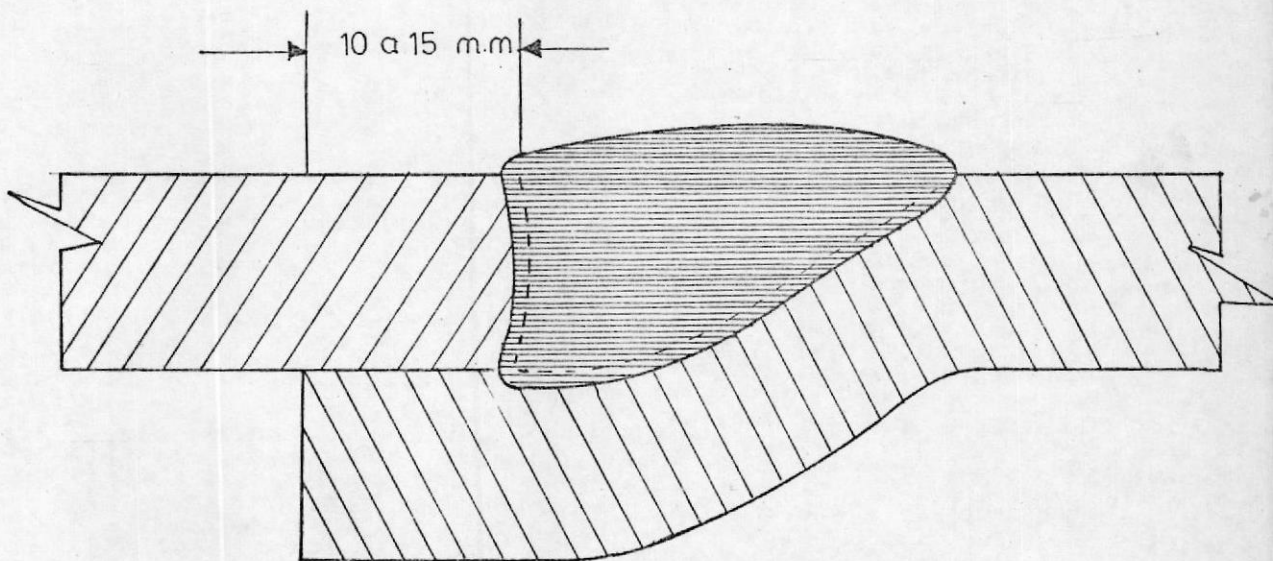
SOLDADURA A TOPE CON TRASLAPO (11)
